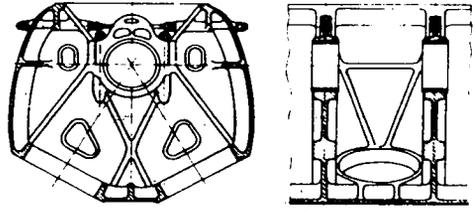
Beispiel für die Formgebung und Verrippung im Quer- und Längsschnitt des Kurbelgehäuses eines V-Motors
